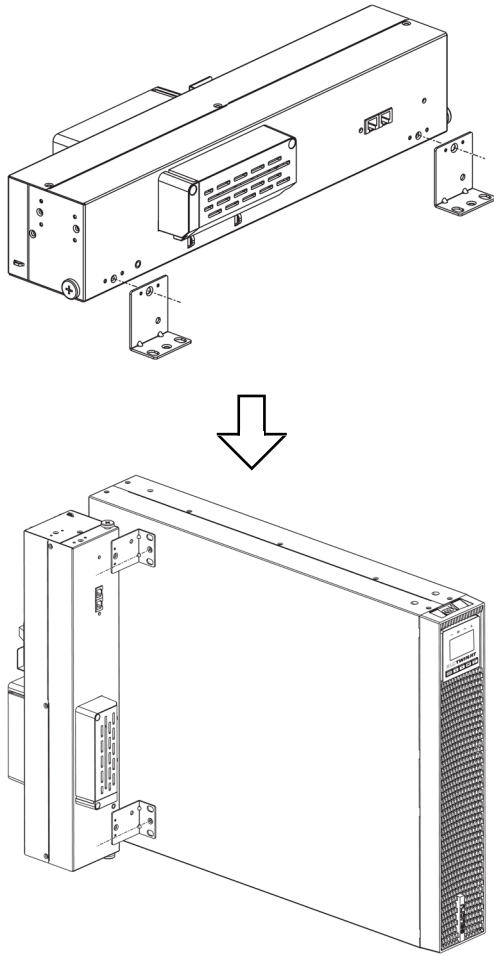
Installation des supports sur le BM-R et fixation de ces derniers sur l'onduleur.
